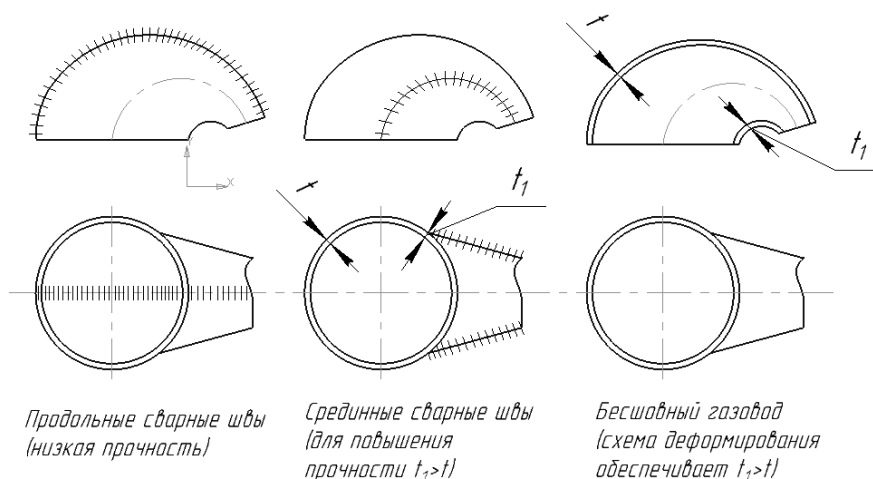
Эволюция технологии газоводов (слева-направо): с боковыми сварными швами; со сварными швами и вставкой; бесшовный
